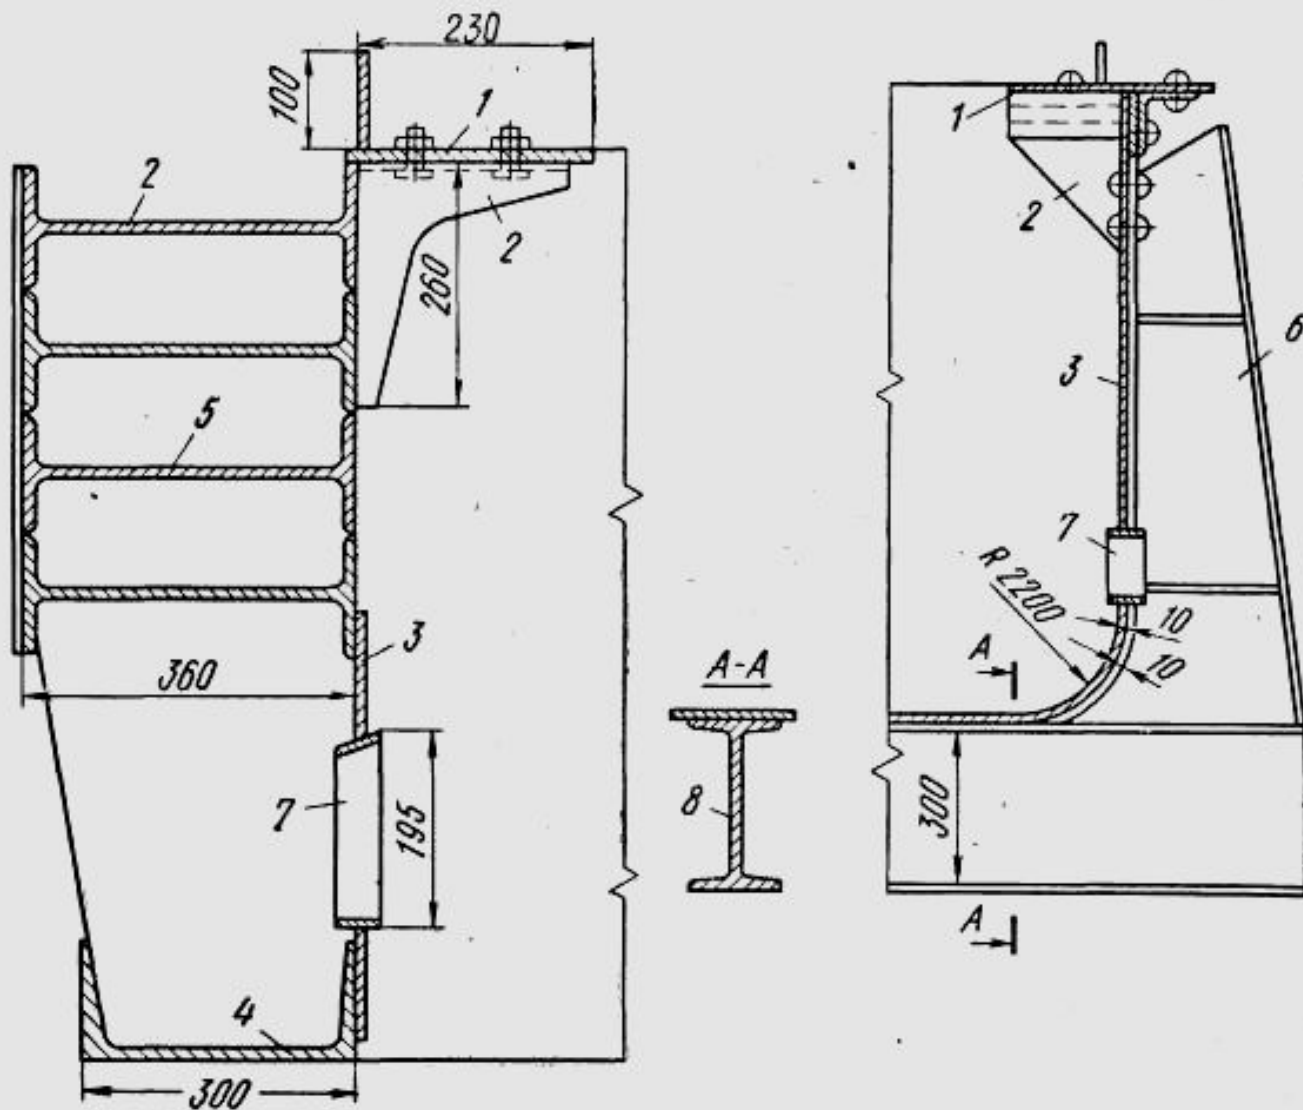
Схема конструкции кожуха алюминиевой ванны:
